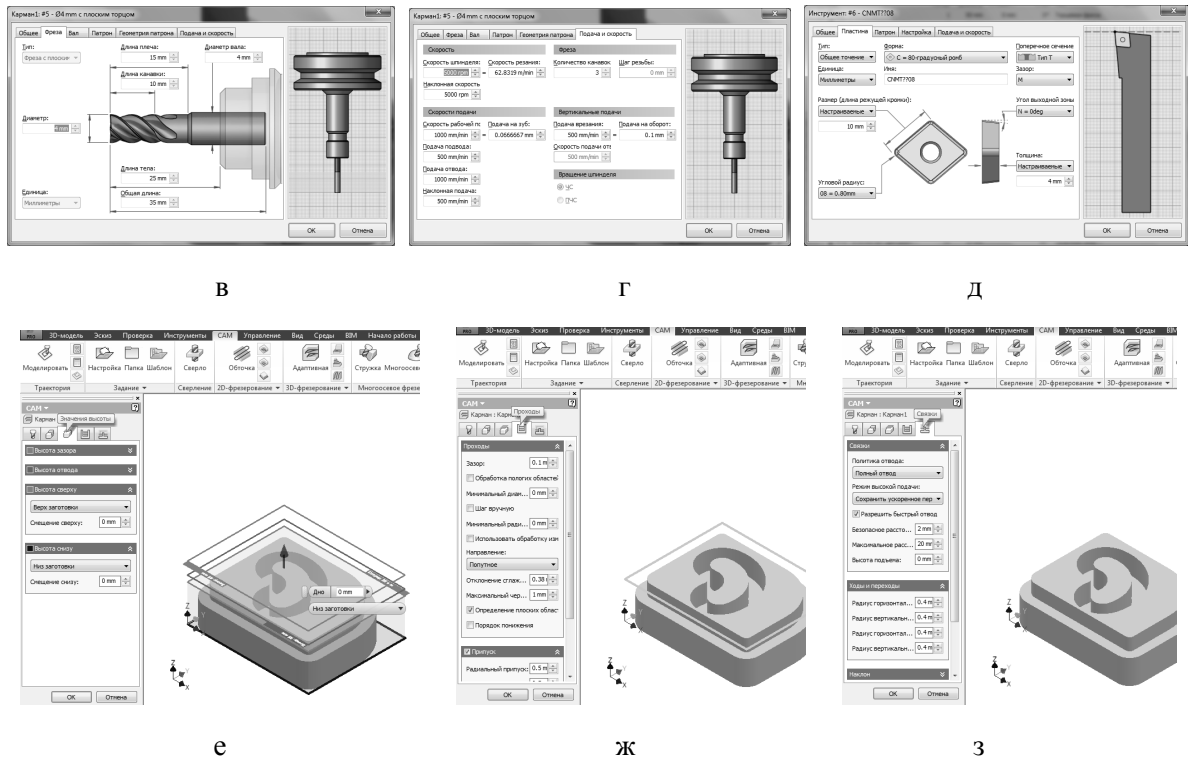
Етапи побудови оброблення заготовки: в, г, д – створення нового інструмента; е – геометрія та висоти оброблення; ж – створення траєкторії руху інструмента; з – завдання положення інструмента (закінчення)
